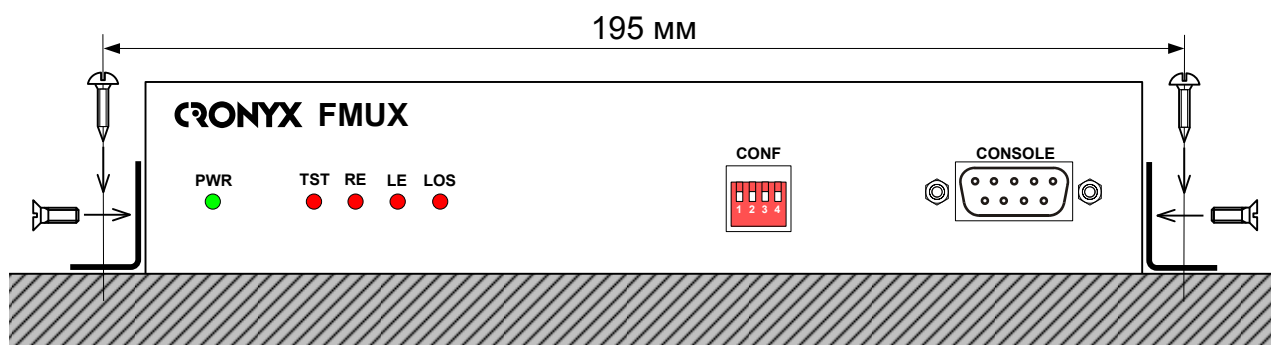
Крепление на стену, вид со стороны передней панели устройства
